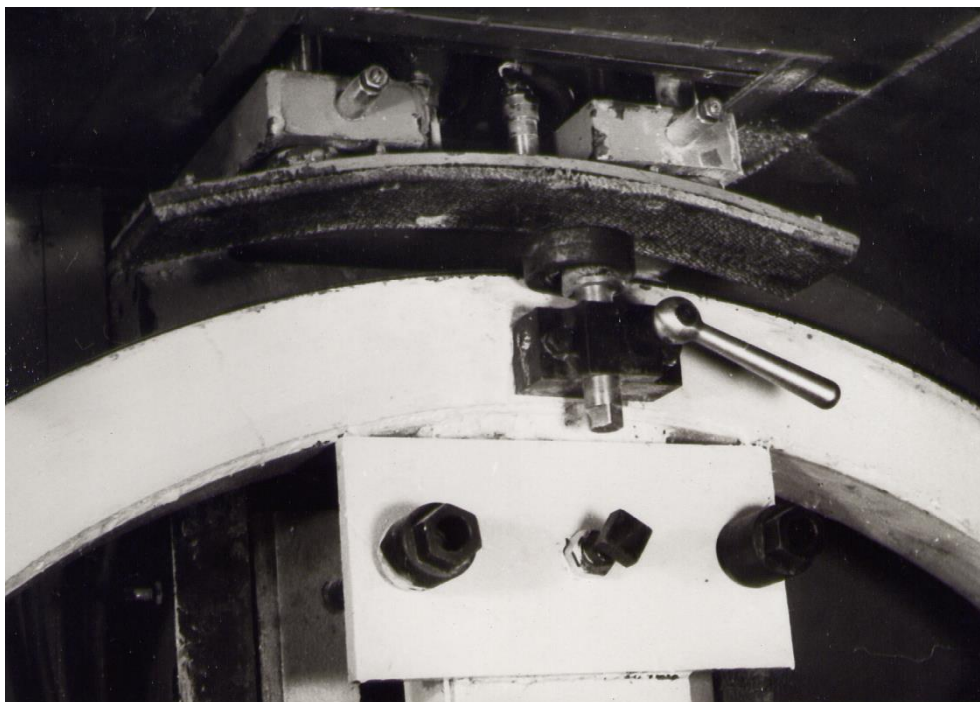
Общий вид устройства для улавливания ленточной пилы при ее обрыве
